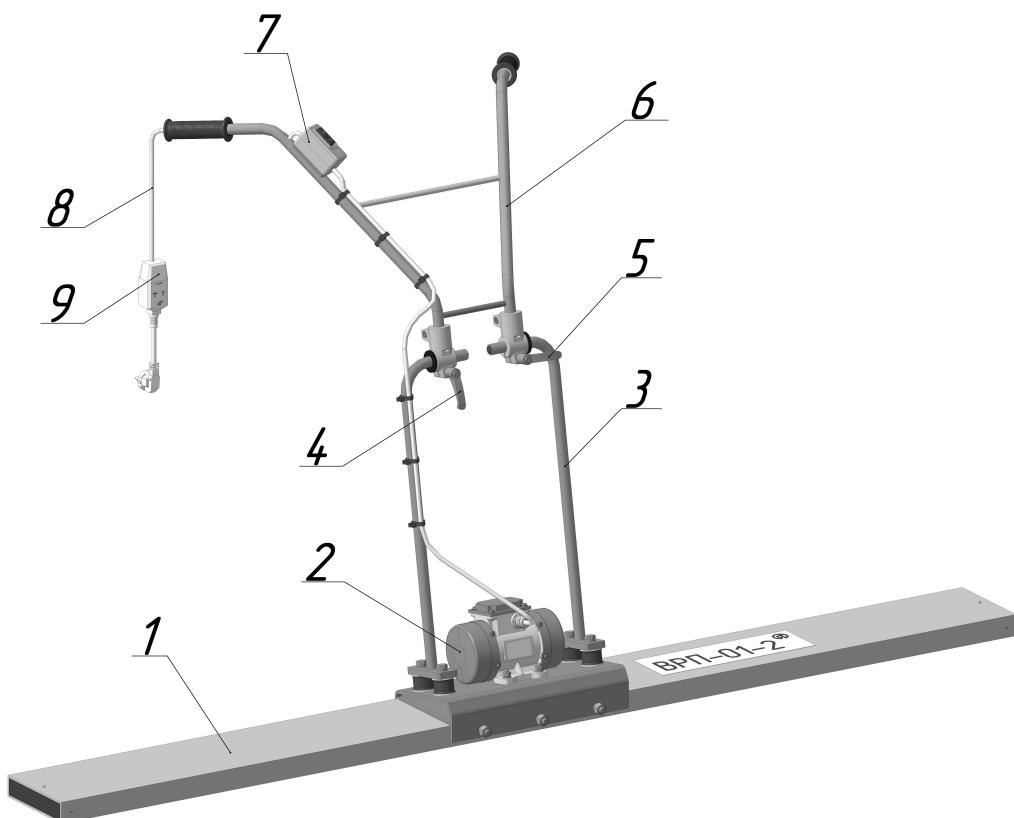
Виброрейка плавающая ВРП-01-2:
